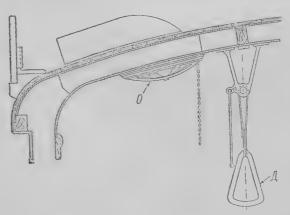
Вентиляция вагона со сводчатой крышей: O — вентиляционное окно, \mathcal{A} — держатель ременный.
